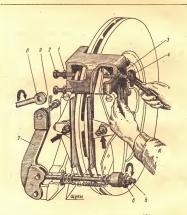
Регулировка ручного тормоза автомобиля ЗИЛ-164: 1, β и δ — контргайки; 2 и 4 — регулировочные болты; δ — гайка; 7 — рычаг; δ — тяга; δ — палец.
